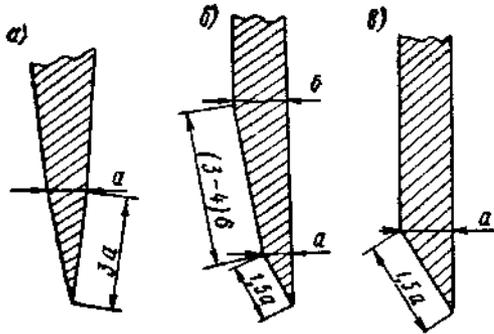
Характер и размеры заточки топора (а), долота (б) и резца рубанка (стамески) (в).
